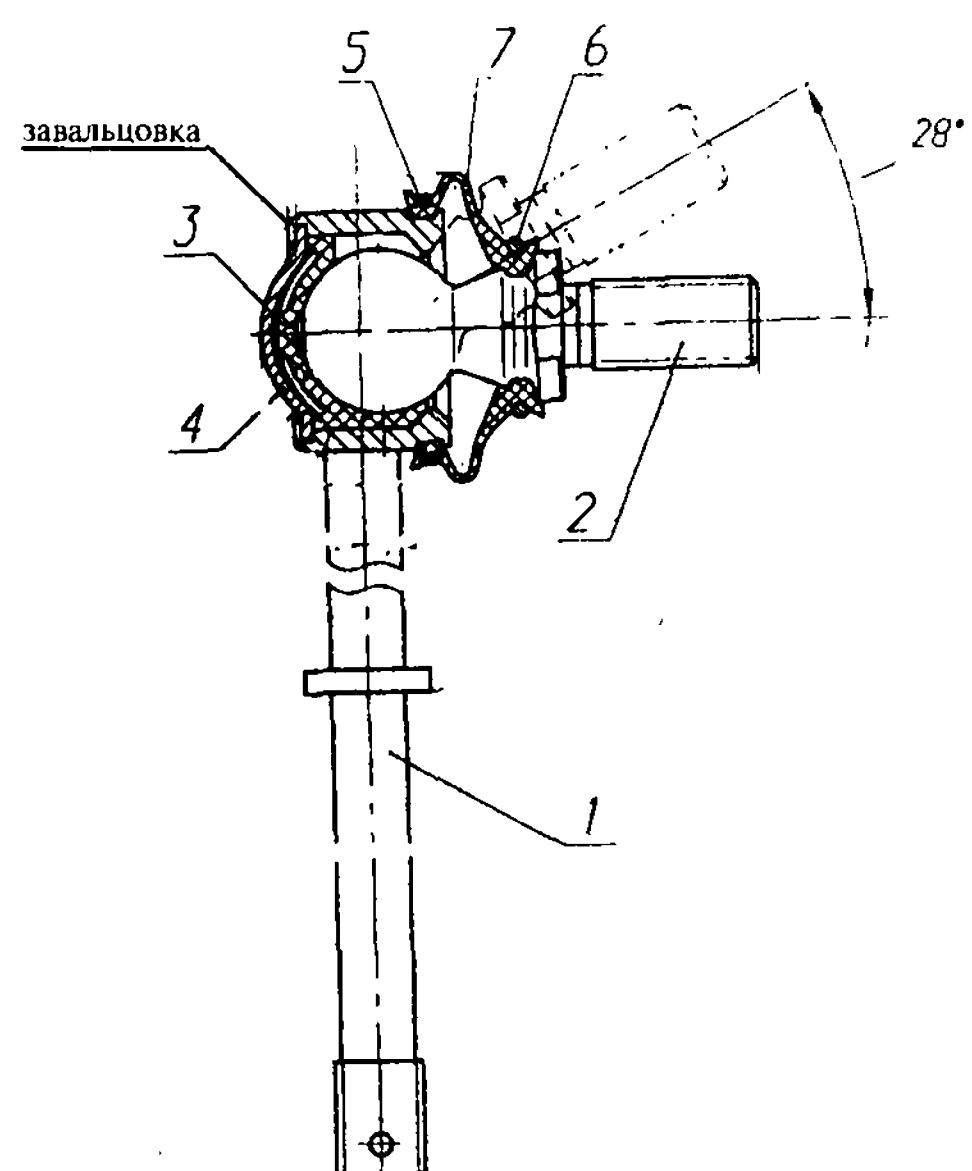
Стойка стабилизатора передней подвески с шаровым шарниром в сборе: 1 – стойка; 2 – шаровой палец; 3 – вкладыш; 4 – крышка; 5 – кольцо пружинное; 6 – кольцо; 7 – уплотнитель
